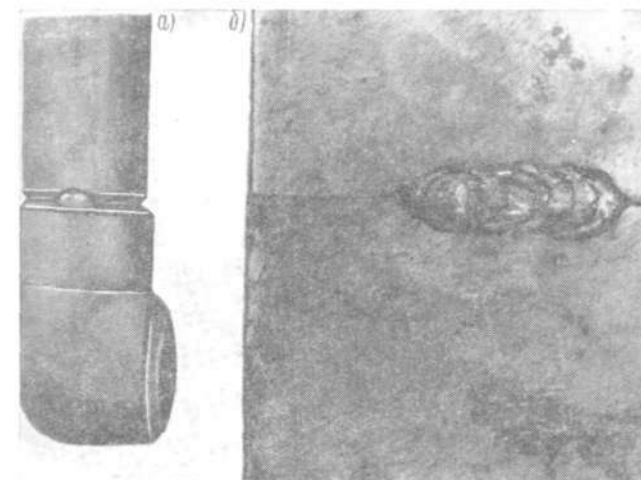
Правильно выполненная заделка кратера на прихватках: а — ручная аргано-дуговая сварка; б — ручная дуговая сварка.
